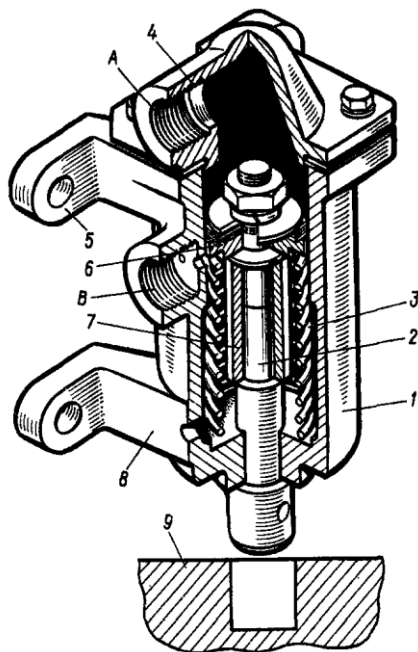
Пневматическая блокировка ПБ-33-02
